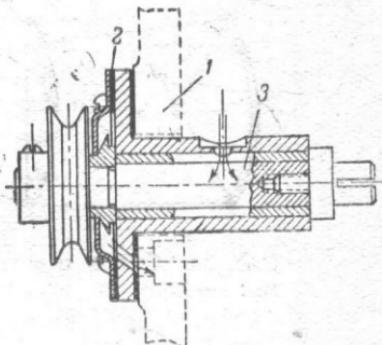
Приводной валик: 1—средняя крышка; 2—подшипник; 3—приводной валик
